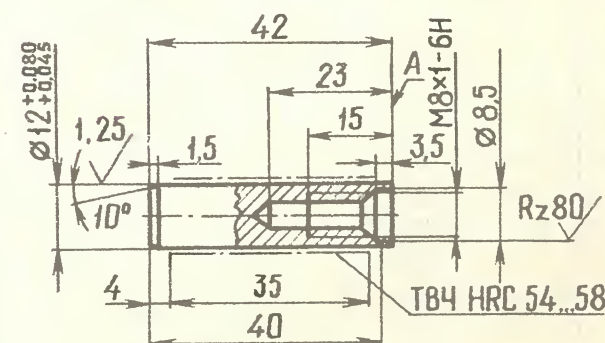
Палец сцепления. Поверхность А обрабатывается окончательно в сборе с маховиком.
